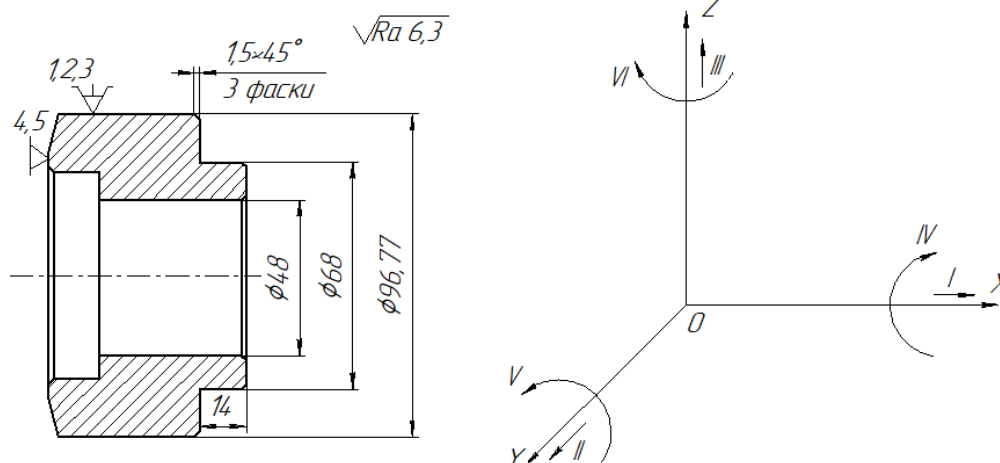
Схема базування заготовки 3-х кулачковому патроні
